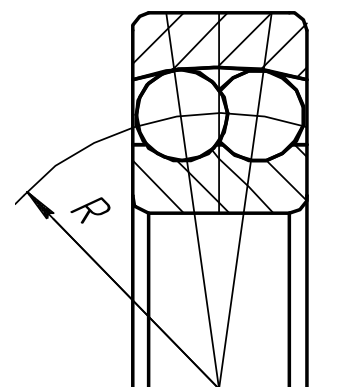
Кульковий радіальний дворядний сферичний підшипник
